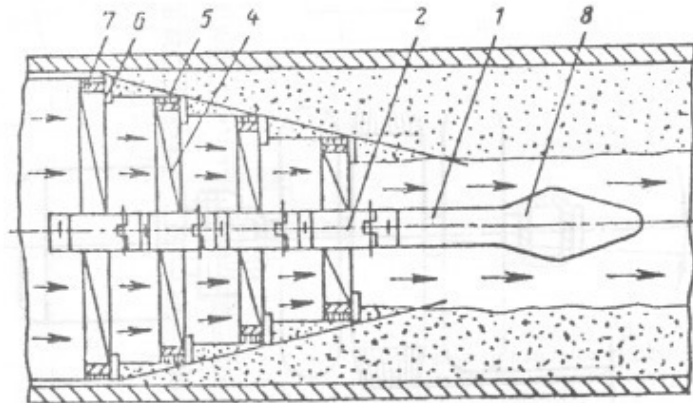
Общий вид очистного устройства для послойного среза загрязнений и чистки криволинейных участков трубопровода, где 1 – гибкий вал; 2- жесткие элементы вала; 3 – соединение «шип-паз»; 4 – турбинки; 5 – обод; 6- очистные элементы; 7 – центрирующие опоры; 8 – направляющая головка.
